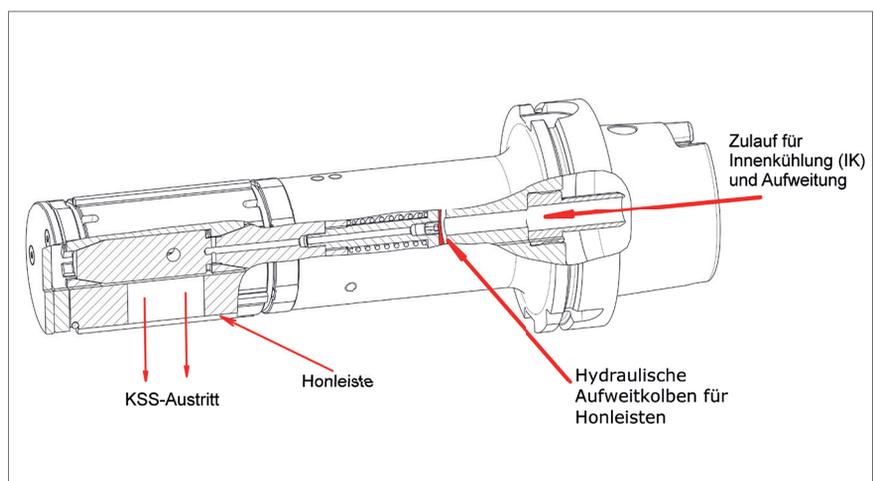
Coollex- Hontechnologie – hydraulisch aufweitendes Honwerkzeug mit Innenkühlung [5]
